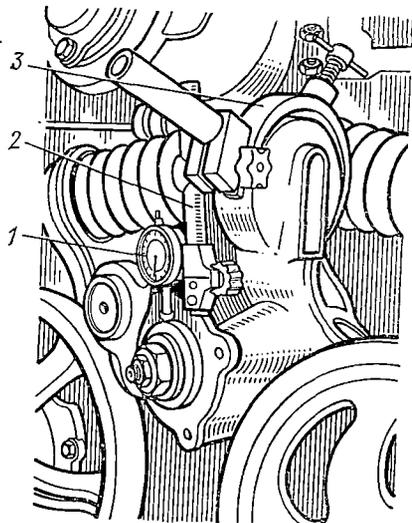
Проверка радиального зазора между втулками и цапфой каретки на тракторе ДТ-75 приспособлением КИ-4850:
